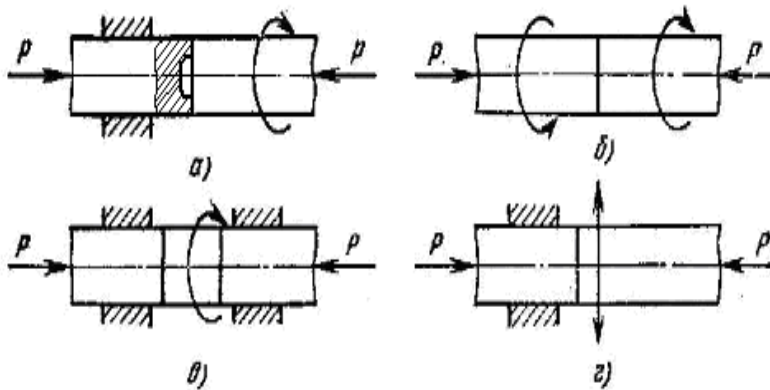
Принципиальные схемы сварки трением: а) вращение одной детали, б) вращение обеих деталей, в) сварка неподвижных деталей с вращающейся вставкой, г) сварка при возвратно-поступательном движении одной детали
